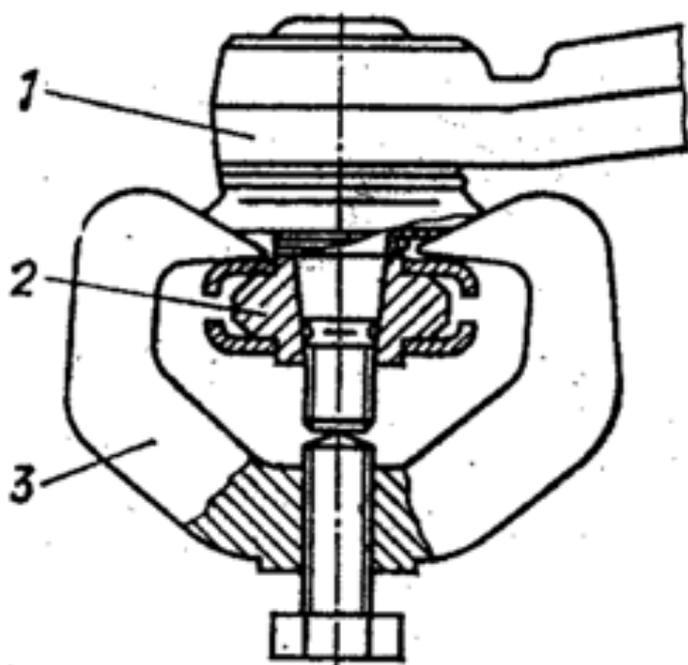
Выпрессовка пальца рулевой тяги: 1 - шарнир рулевой тяги; 2 - кронштейн стойки передней подвески; 3 - съемник.
